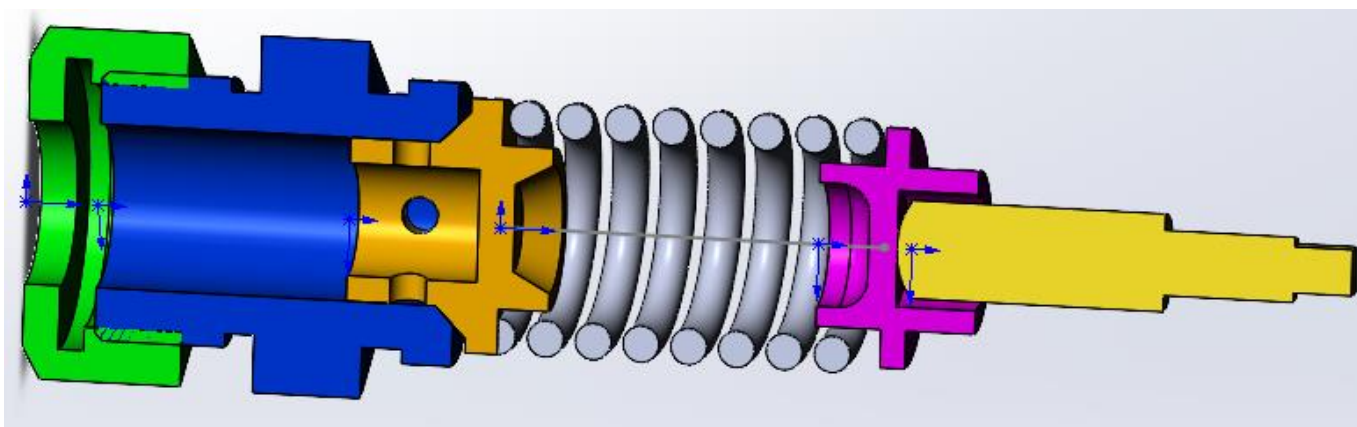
Вид сборки, после вставки детали «Винт»
